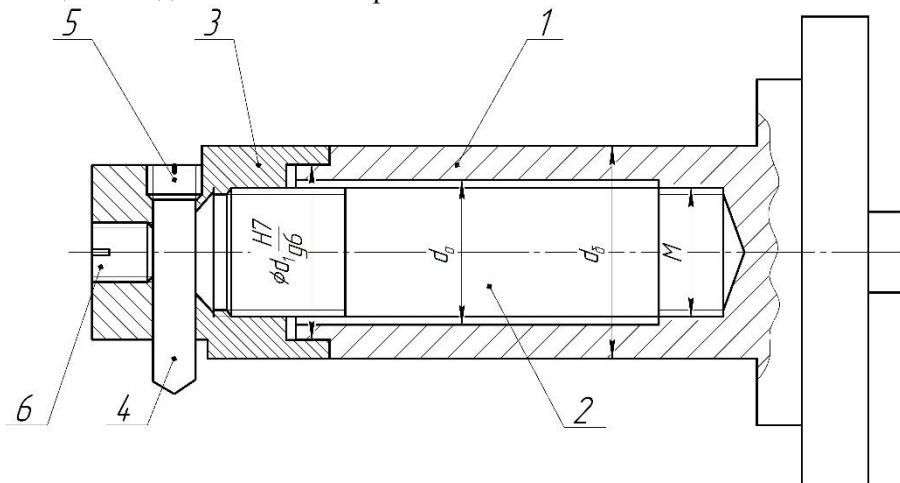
Конструкція борштанги з попереднім стисненням: 1 - корпус; 2 - шпилька; 3 - різцеутримувач; 4 - різець; 5, 6 - регулювальні гвинти.
